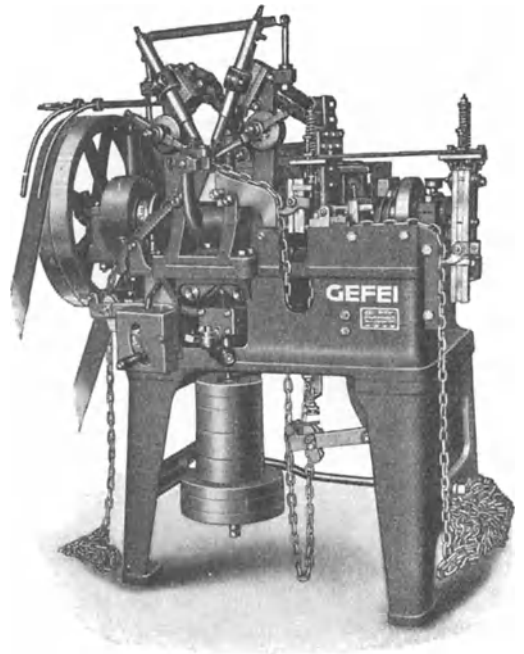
Ganz selbsttätig arbeitende Kettenschweißmaschine.
